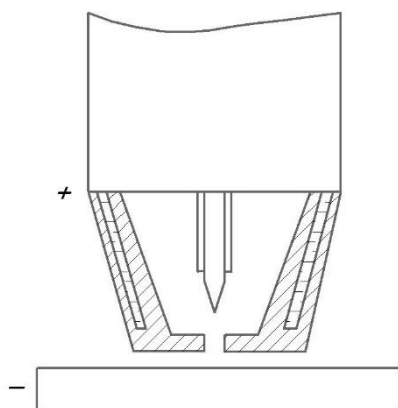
Схема плазменной сварки на обратной полярности
